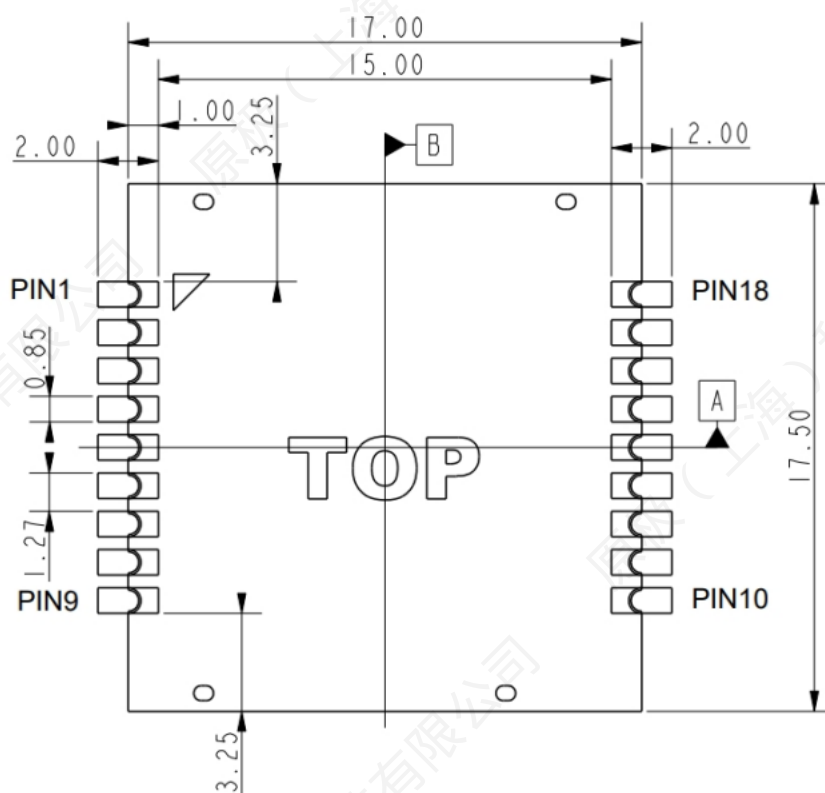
推荐焊盘尺寸 (单位: mm)
